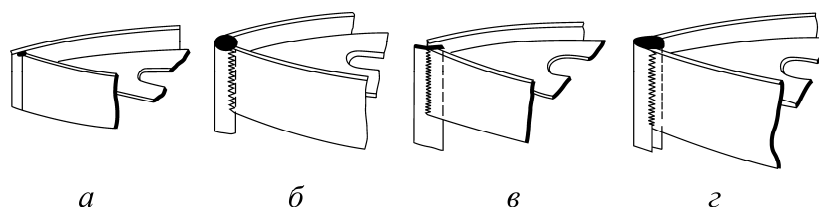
Узлы соединения обшивки руля на кормовой кромке
